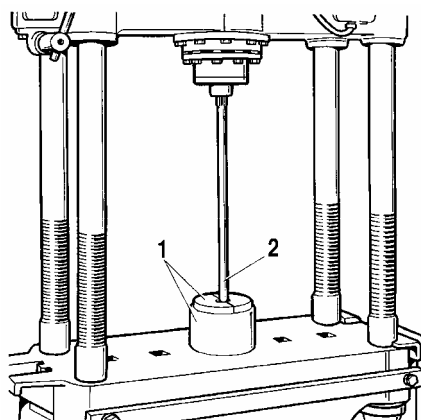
Выпрессовка запорного кольца подшипника полуоси:
